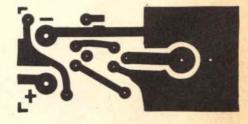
Lato rame del circuito stampato del sincronizzatore per flash di figura 12.
